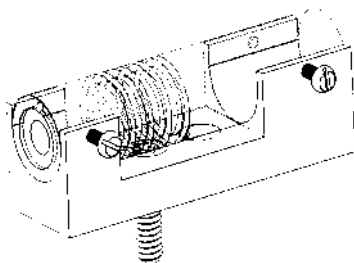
модель крепежа лазера в цилиндрическом корпусе
